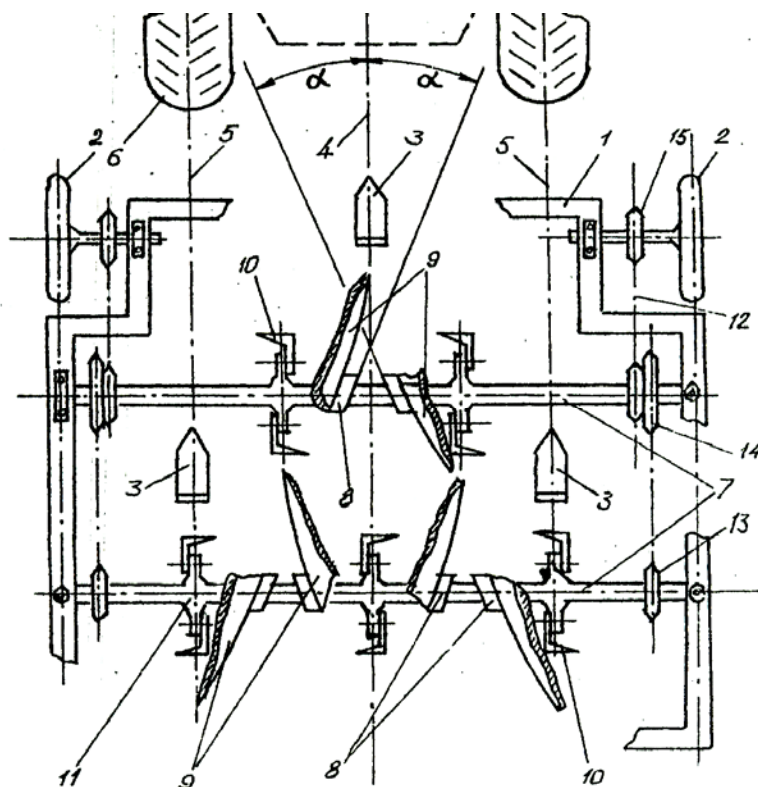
Схема конструкции дискового плуга-рыхлителя (вид сверху):
